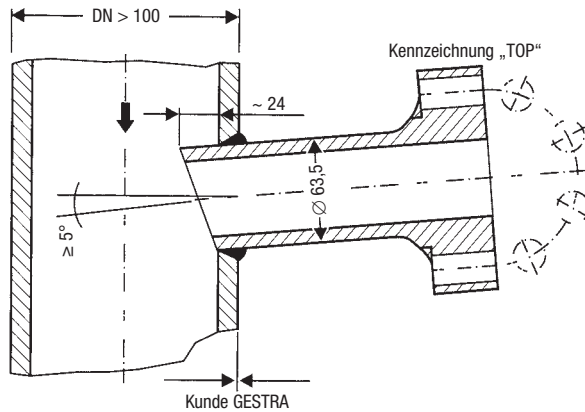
Einschweißen des Anschlussstutzens in Rohre DN > 100
